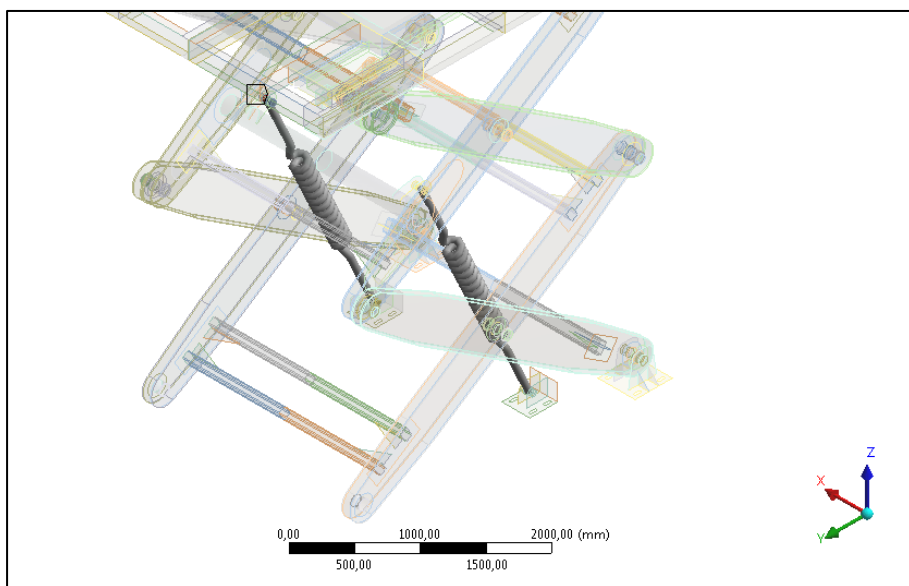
Zobrazení činného prostoru válce pro horní a dolní polohu
